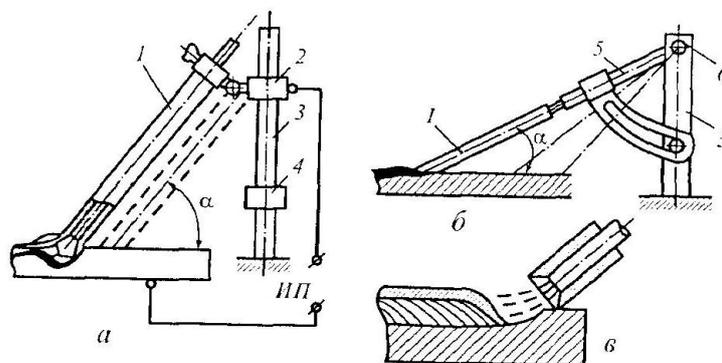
Схема сварки наклонным электродом:
